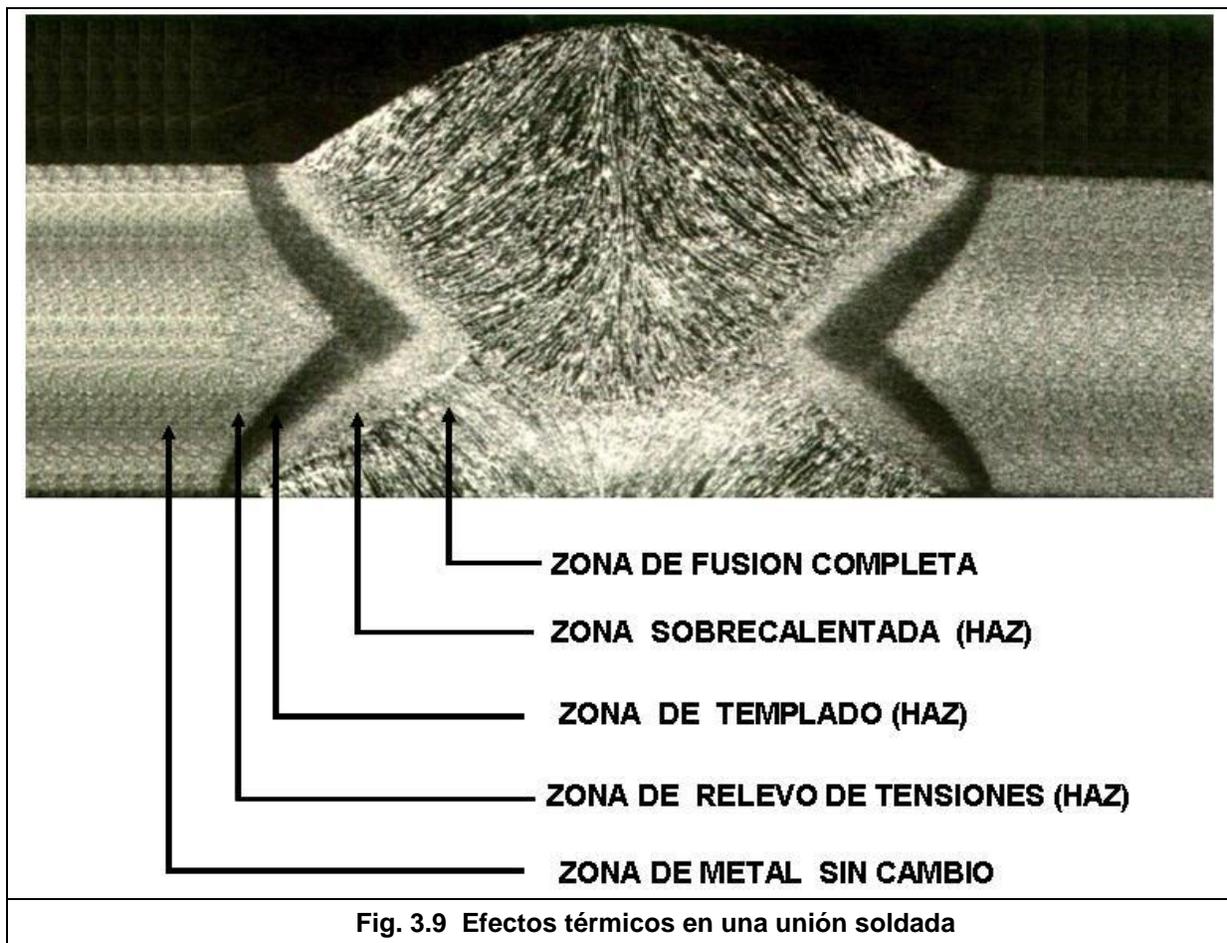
Efectos térmicos en una unión soldada
